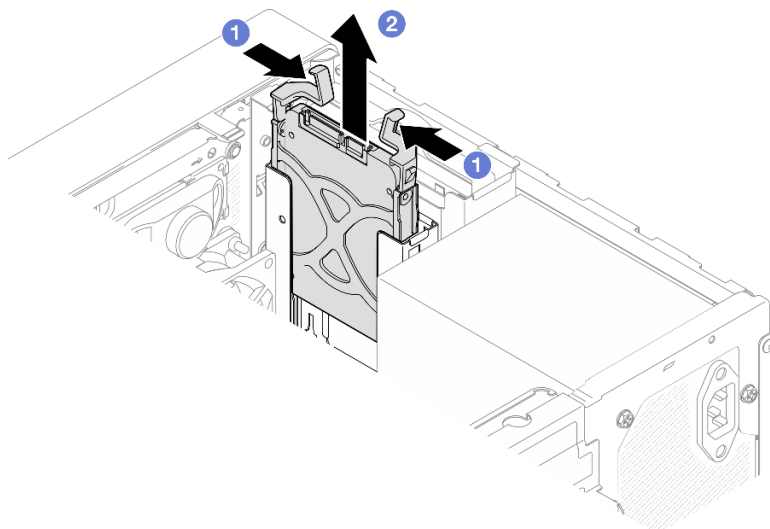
Entfernen einer Laufwerkbaugruppe aus Laufwerkposition 1
